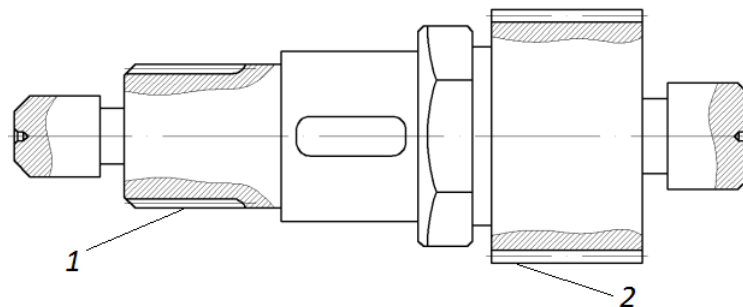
Вал шліцьовий циліндричного редуктора
